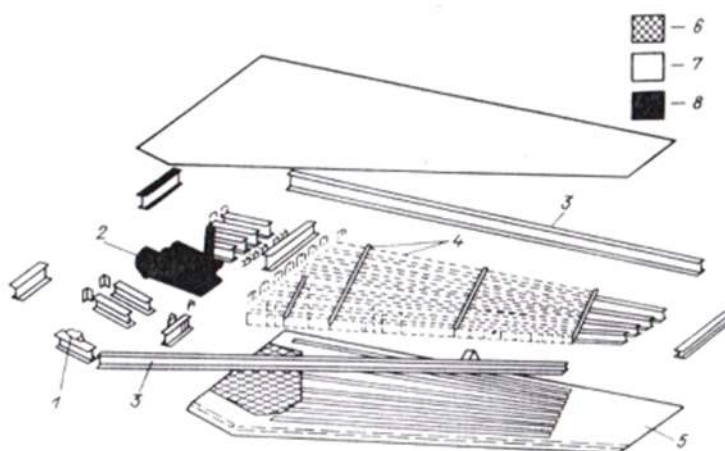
Виготовлений з композита горизонтальний стабілізатор:
